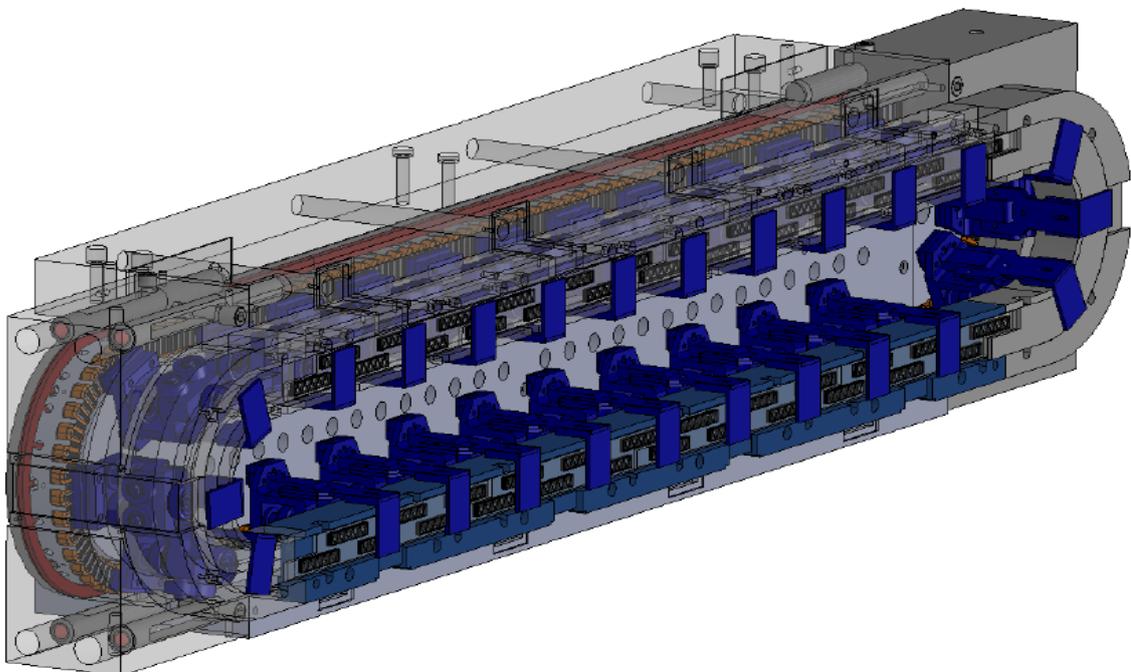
Ovalstatormotor für die Verpackungstechnik mit einer Vielzahl unabhängig ansteuerbarer Läufer /42/
